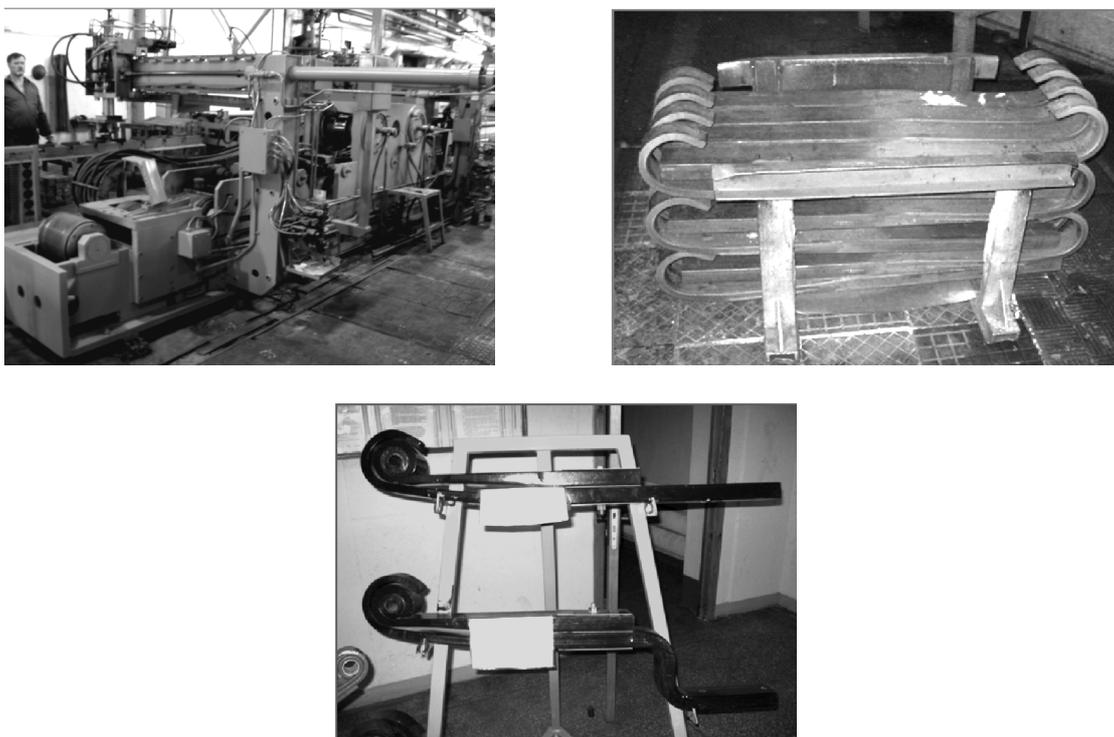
Прокатный стан и заготовки детали опор пневмоподвески
